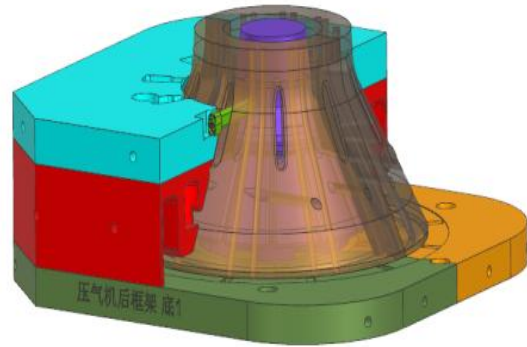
燃气轮机不锈钢机匣 3D 打印型芯空间网格化结构示意图
